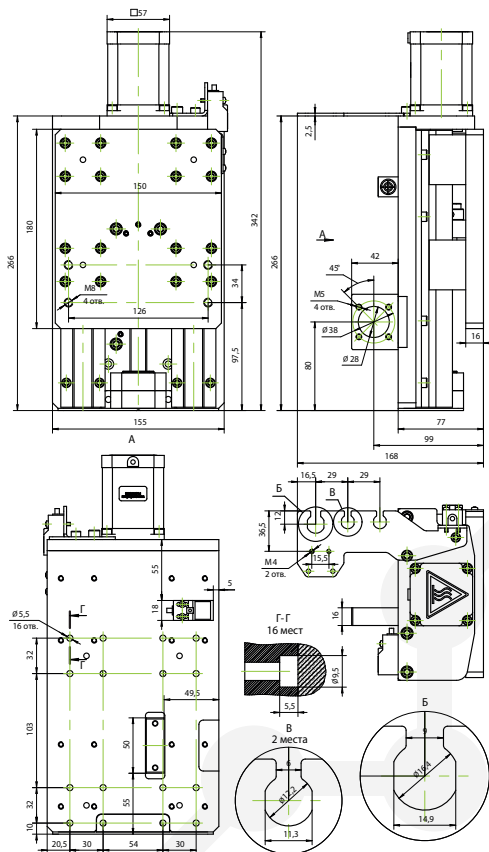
Габаритный чертёж модуля оси Z RY-Z100-0306
